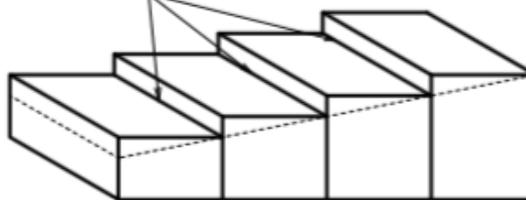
Сокращение длины сварных швов и уменьшения веса конструкции благодаря использованию разнотолщинных листов.
